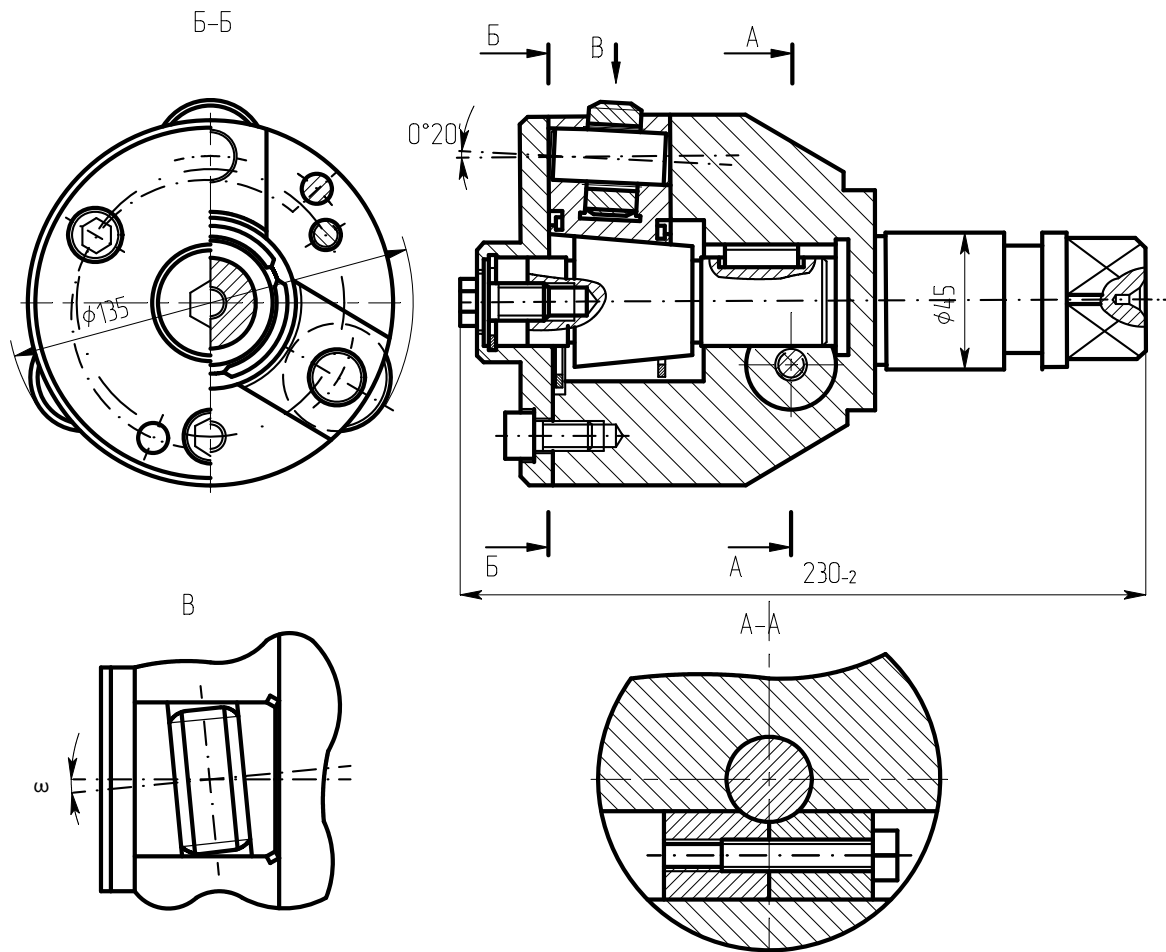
Регульована головка для накатування внутрішньої різьби M135×2
